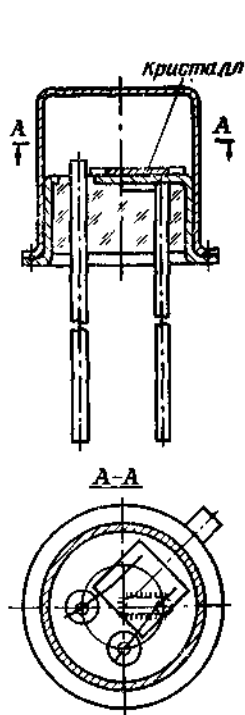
Конструкция корпуса КТ-21. Вариант для монтажа кристалла непосредственно на фланец корпуса.
